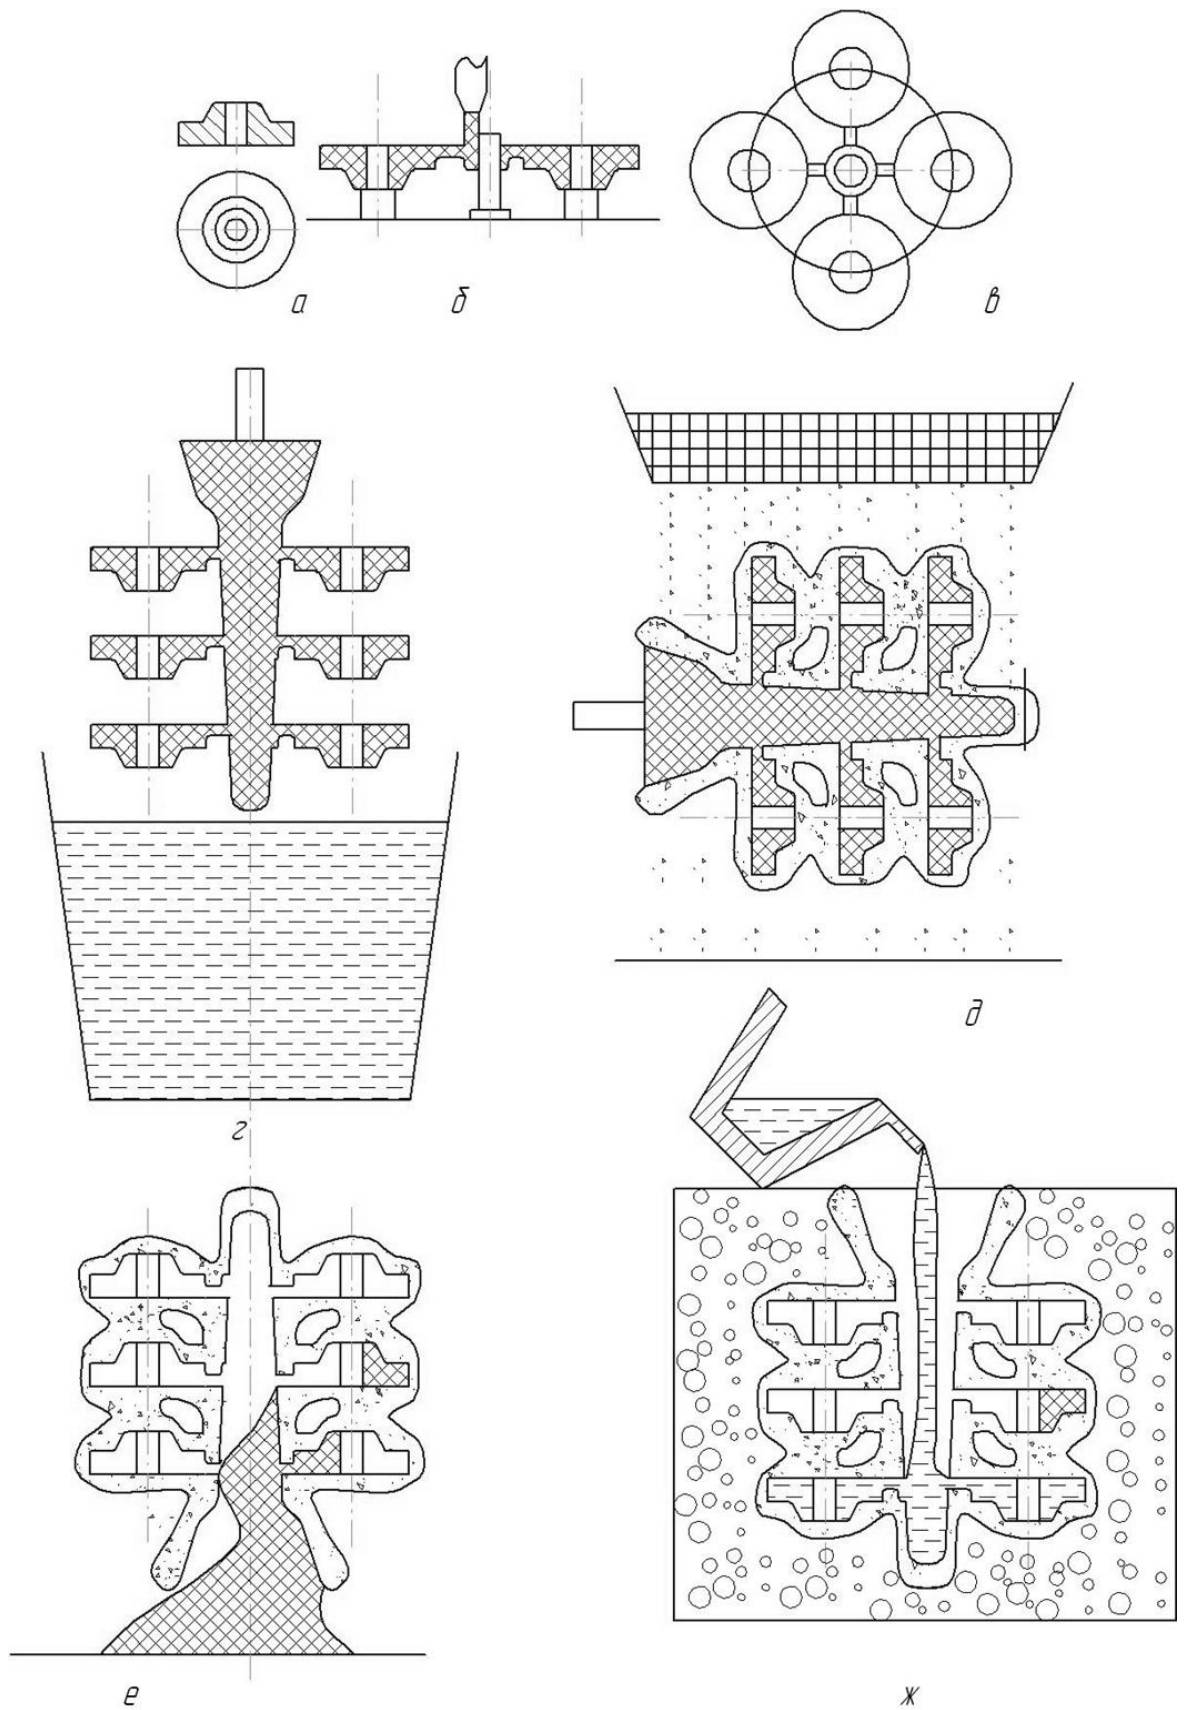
Изготовление отливок способом литья по выплавляемым моделям
